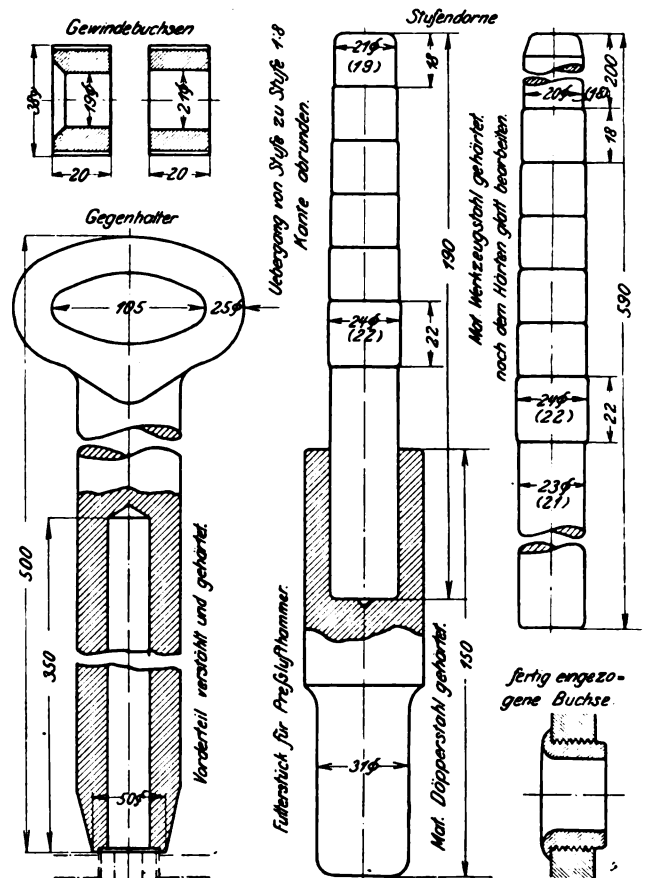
Werkzeuge und Buchsen zum Ausbuchverfahren.
